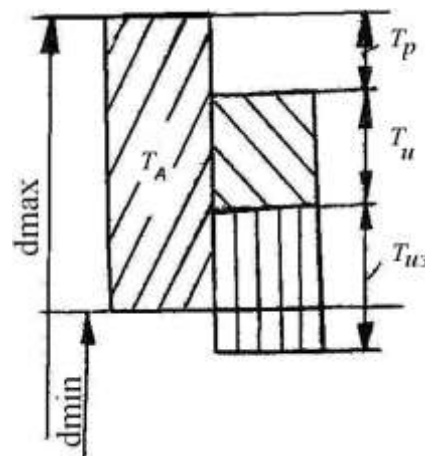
Схема расположения допусков на диаметр развёртки
